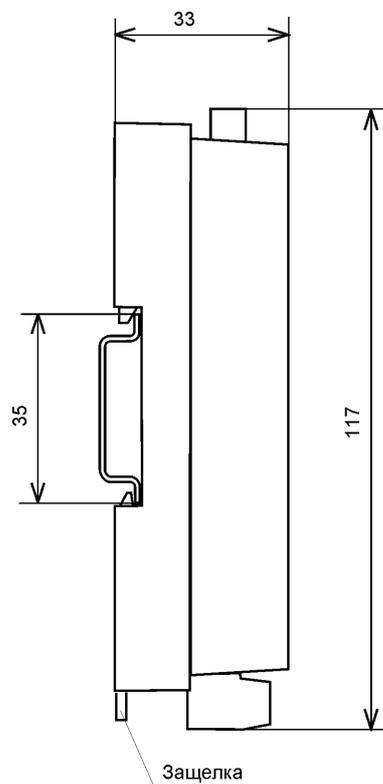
Габаритный чертеж модуля с креплением к DIN-рейке. Вид сбоку.
